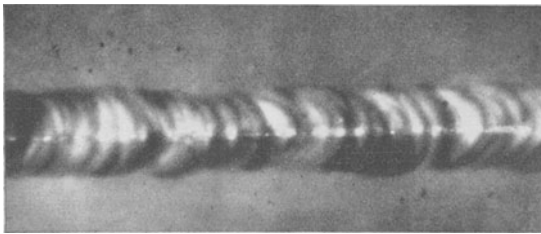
Röntgenbild einer nicht einwandfreien Rechtsschweißung.
